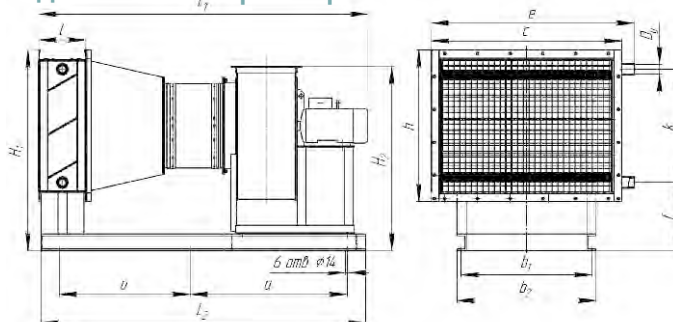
Габаритные и присоединительные размеры воздухонагревательных установок типа ВТУ.
